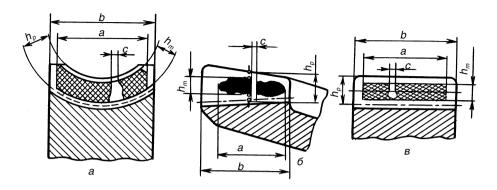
Пятно контакта зубьев в передаче: а — червячного колеса; 6 — конического зубчатого колеса; в — цилиндрического зубчатого колеса
